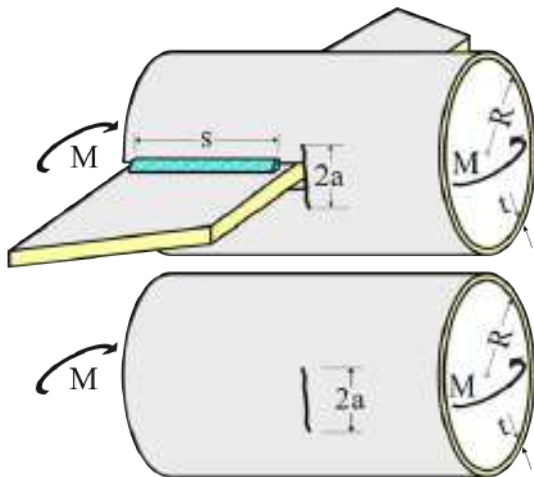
Configuraciones de carga y de fisura consideradas para predecir el límite de fatiga de la unión soldada chapa-tubo.
